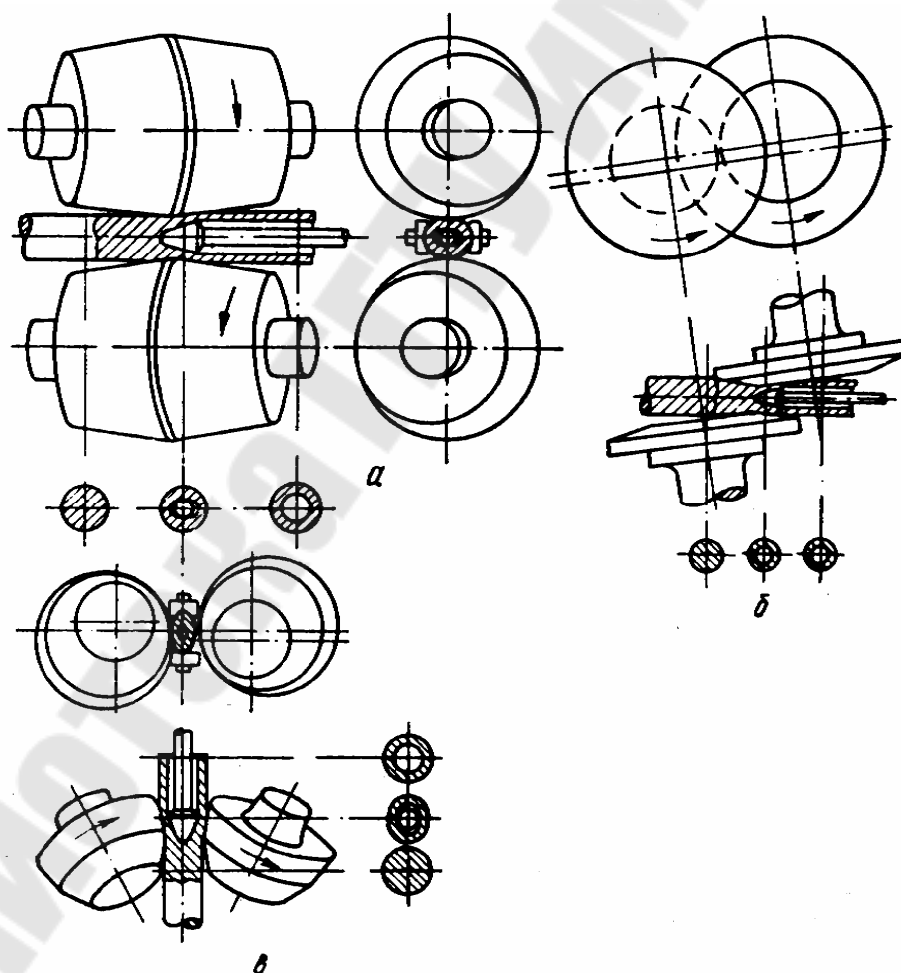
Схемы прошивки на станах поперечно-винтовой прокатки
